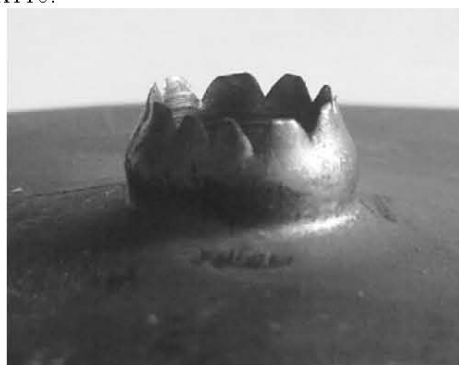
Нижняя часть крепежного элемента (подача 160 мм/мин; инструмент с конической формой рабочей части)
